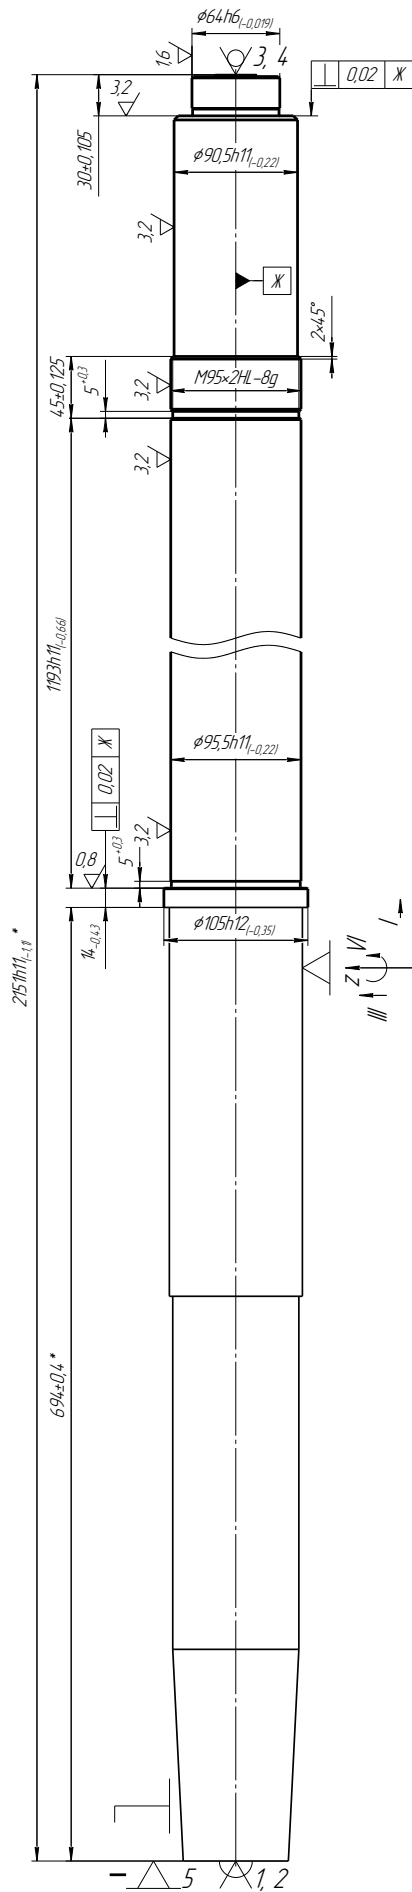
Схема установки заготовки на жестких центрах
